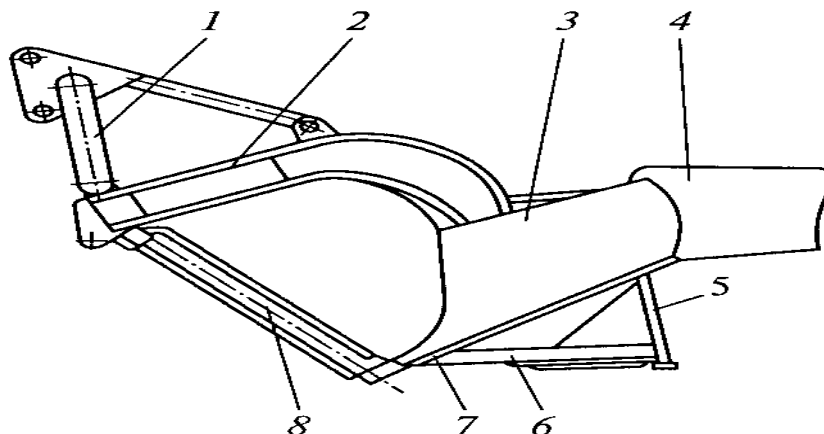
Плуг-канавокопатель ПКЛН-500А: 1 — навесное устройство; 2 — рама; 3 — корпус; 4 — бермоочиститель; 5 — подставка; 6 — опорная лыжа; 7 — нож-откосник; 8 — черенковый нож
